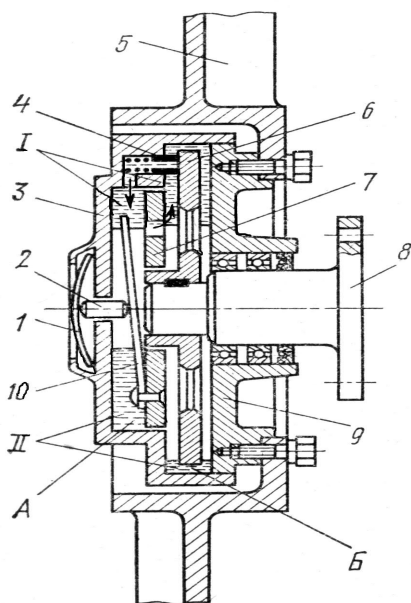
Вязкостная муфта фирмы «Холсет»: I и II – полости; 1 – биметаллическая пластина; 2 – штифт; 3 – корпус; 4 – трубка; 5 – лопатки; 6 – ведущий диск; 7 – разделительный диск; 8 – ступица; 9 – ведомый диск; 10 – пластинчатый клапан.
